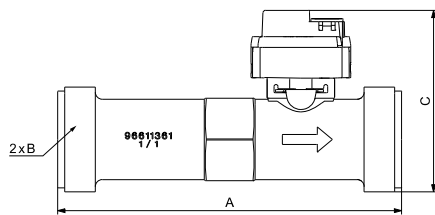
Abmessungen des Sensors VFS 10-200 l/min (ohne Adapter)
